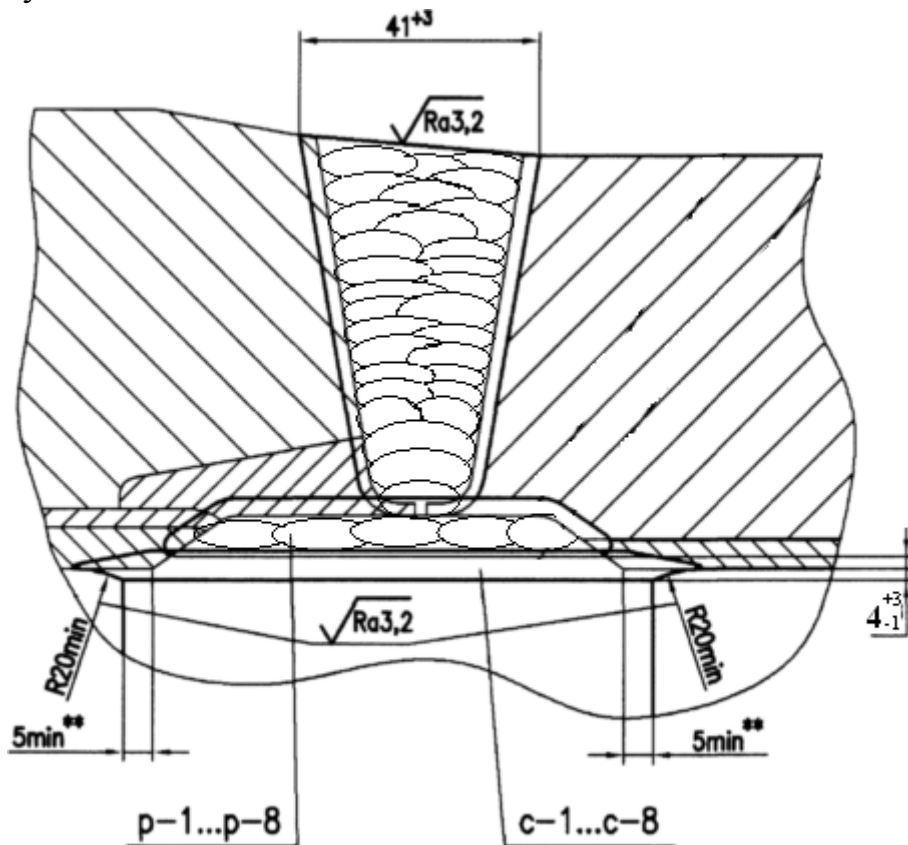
Выполнение плакирующего слоя на сварном соединении ГЦК с патрубком корпуса реактора
